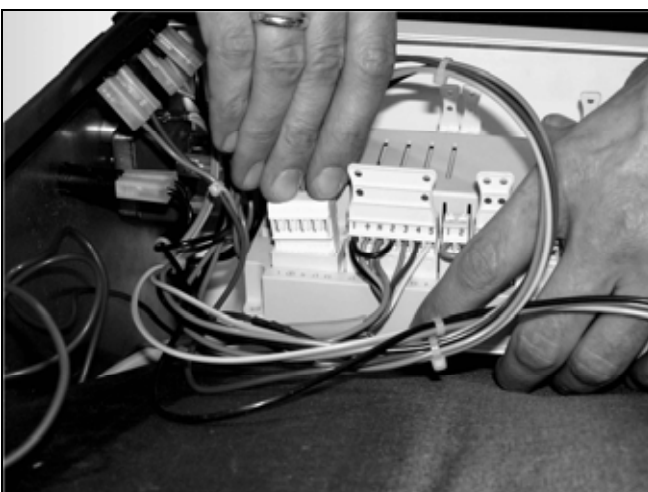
Den Stecker für die Spannungsversorgung in den Kesselregler einstecken.
